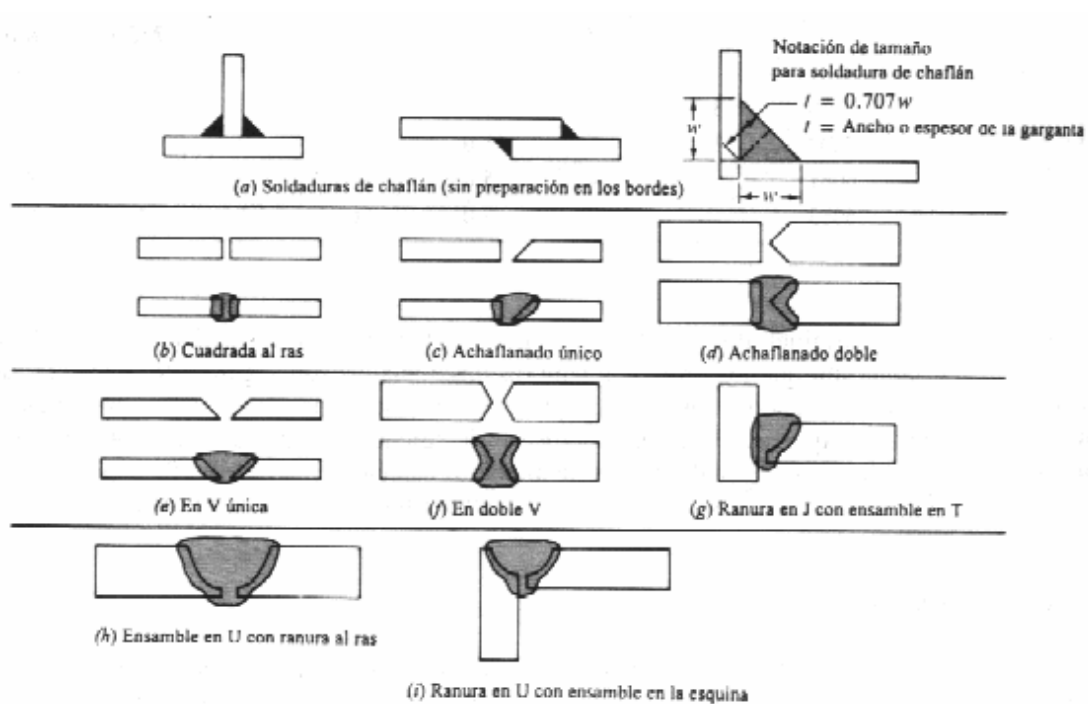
Algunos tipos de soldadura, se muestra la preparación de los bordes.
